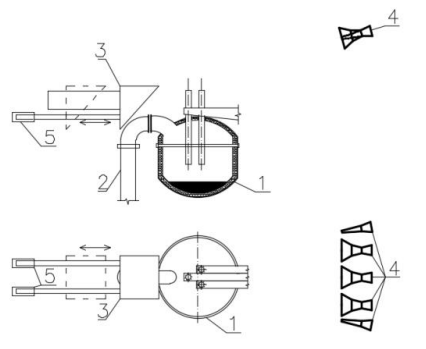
Схема опытно-промышленной установки для улавливания неорганизованных пылевых выбросов от электросталеплавильной печи: 1 – дуговая электросталеплавильная печь; 2 – газоход местного отсоса от четвертого сводового отверстия; 3 – подвижной вытяжной зонт; 4 – аэраторы
